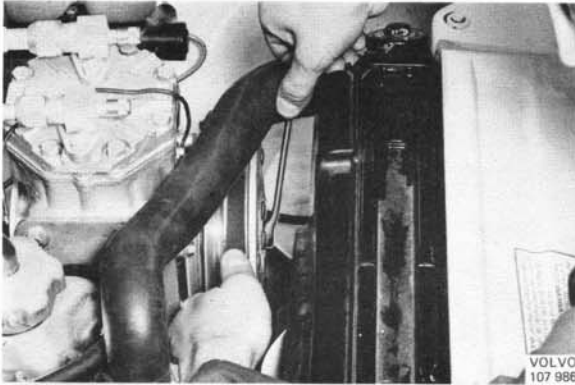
Festzug der Zentrumschraube für die Kompressorriemenscheibe
